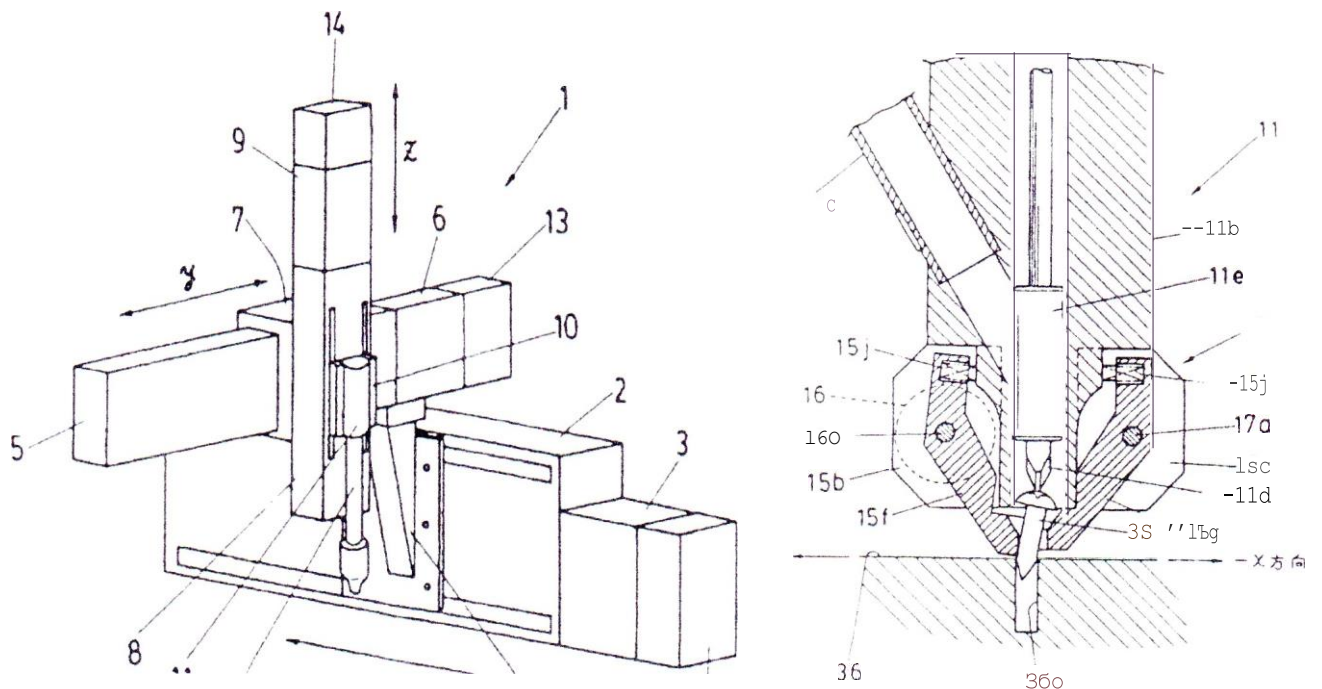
Податлива головка для загвинчування гвинтів: 1- зовнішній вигляд; 11- головка; 11с- лоток подачі гвинтів; 11d- викрутка; 15- важелі (тримачі гвинтів); 15j- здавачі зміщення; 35- гвинт; 36а- різьбовий отвір.
